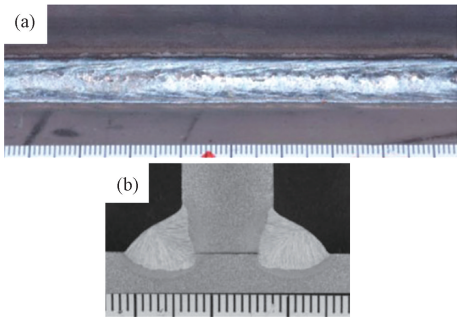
焊缝成形^[24] (a) 焊缝宏观形貌; (b) 焊缝横截面形貌
